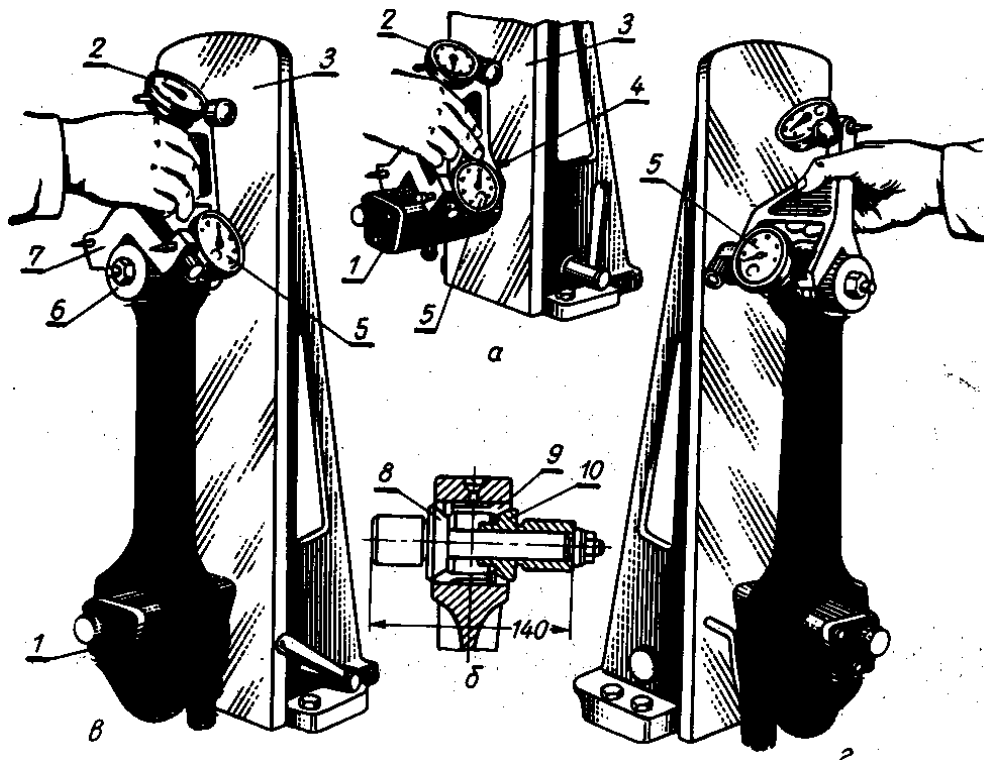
Приспособление для проверки шатуна на скрученность и изгиб:
